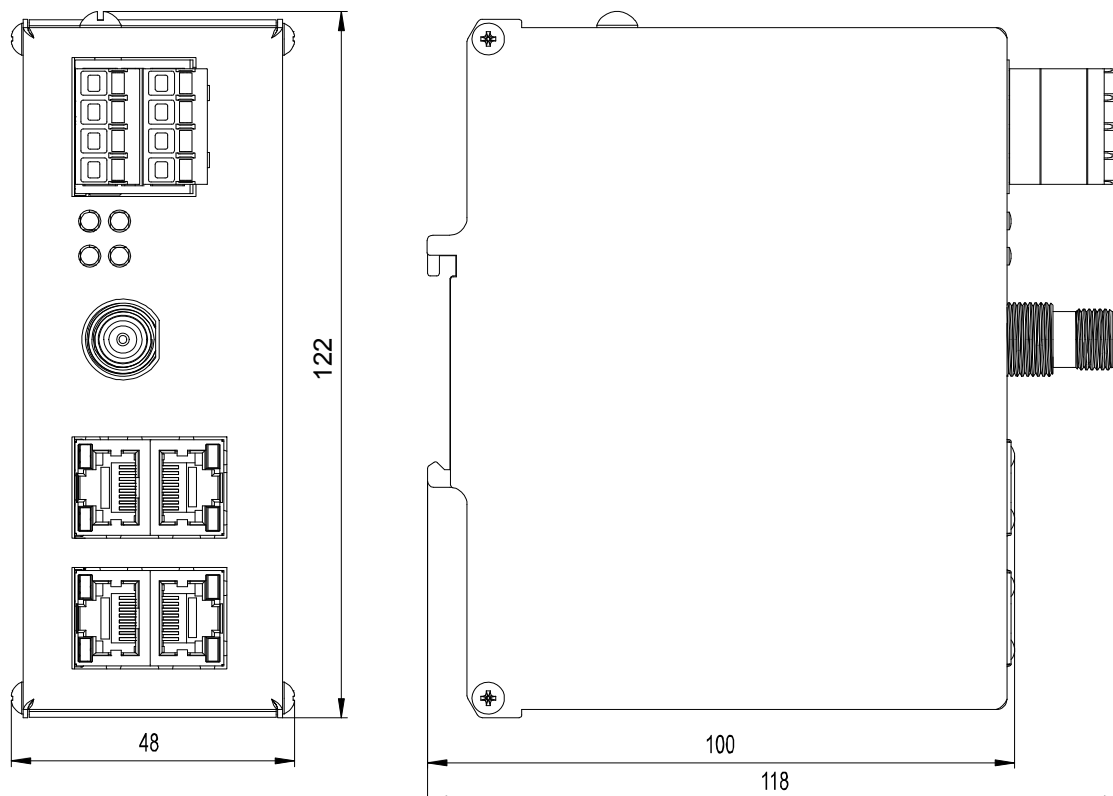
Чертеж общего вида S351 с указанием габаритных и присоединительных размеров
